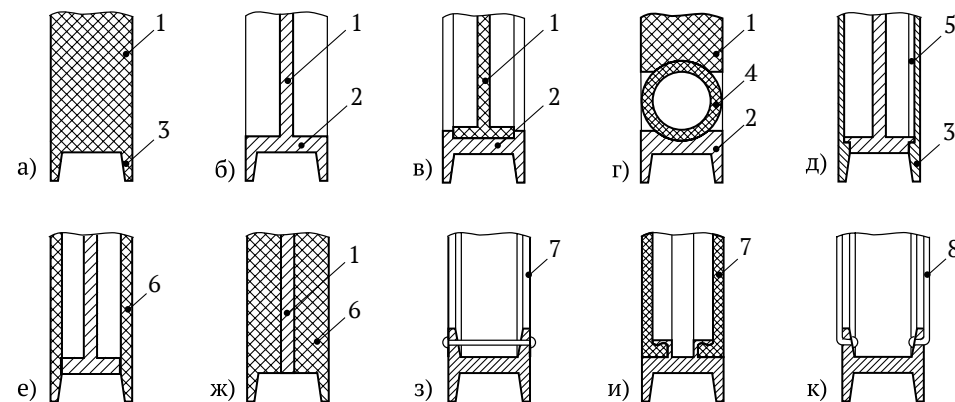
Конструкция опорной части колеса (варианты):
